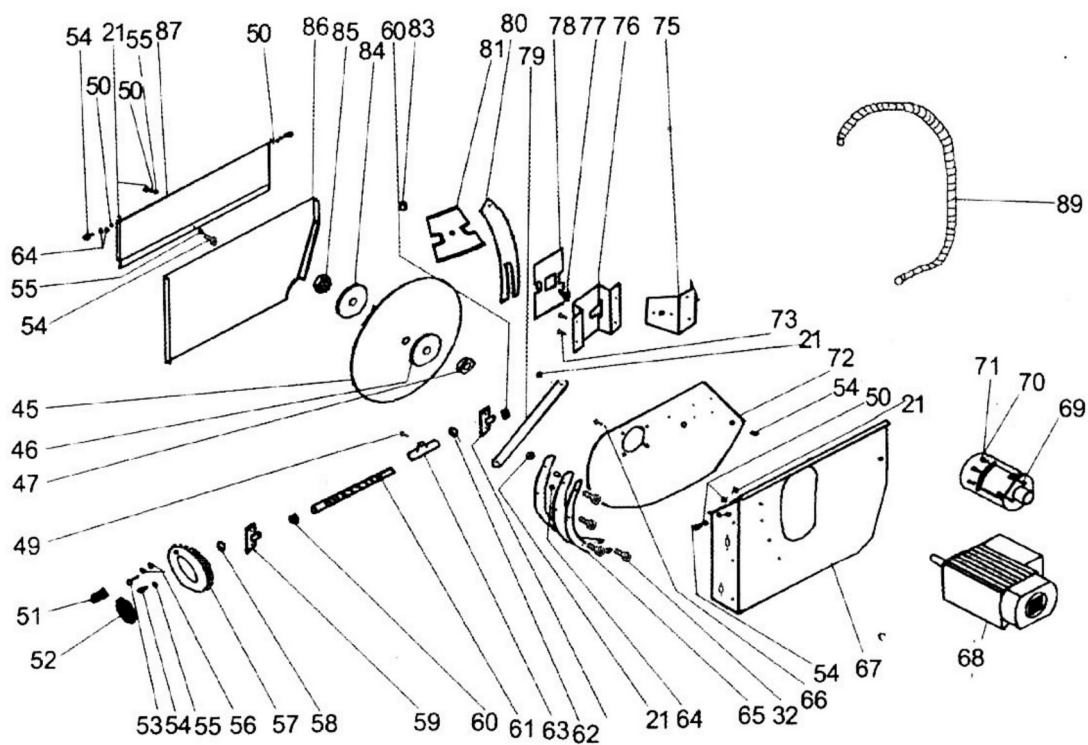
Vista explodida — cârter de aparas, disco e motor
